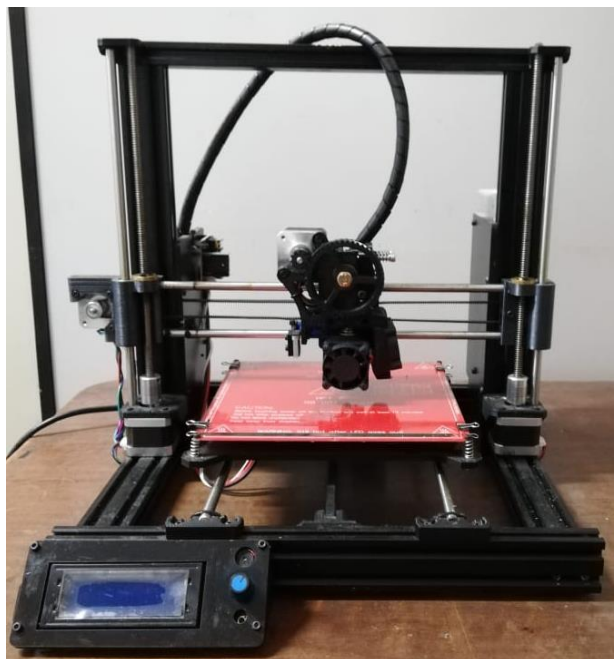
Impressora 3D Graber I3 - Tec 3D.
